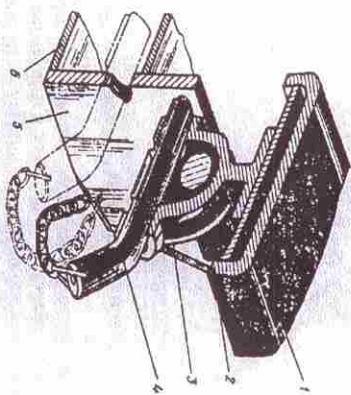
Формы платформы на раме: 1 — рама; 2 — платформа; 3 — передняя опора; 4 — задняя опора; 5 — запорный палец
